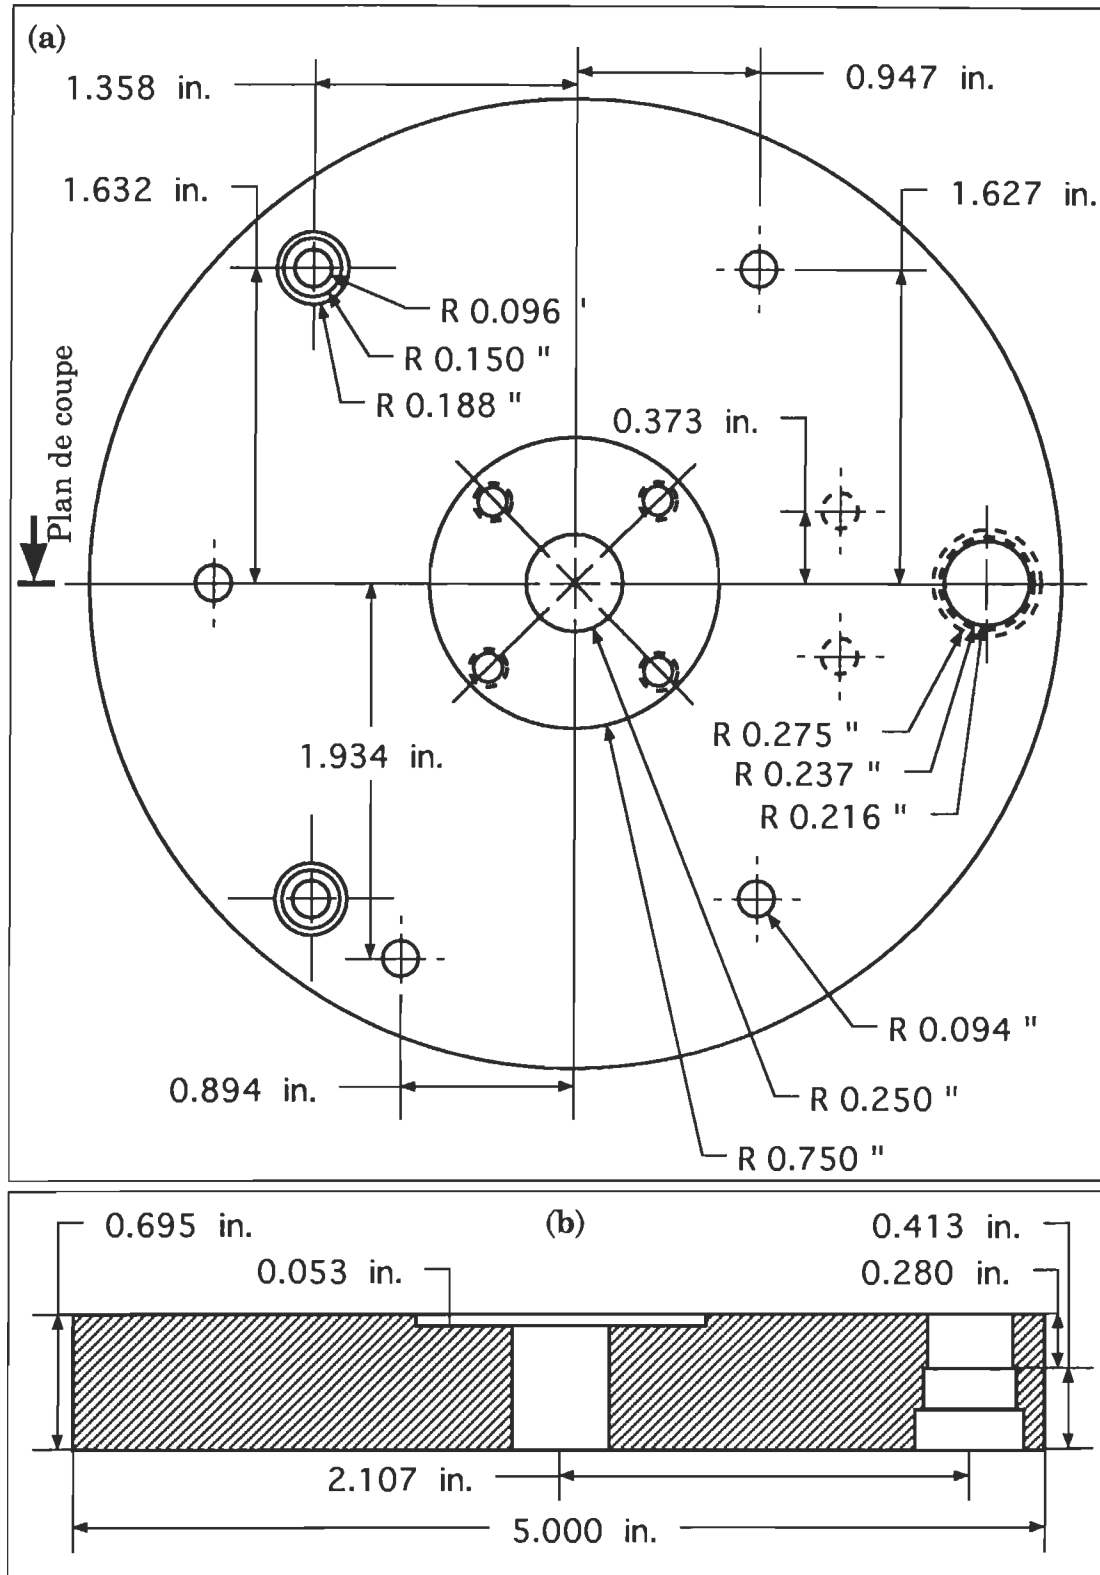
Vue de dessus [a] et vue de coupe [b] du support fixe de la tête AFM.
